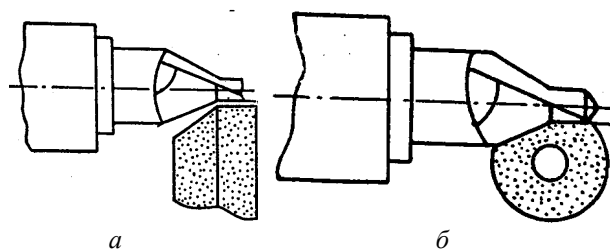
Схема обработки сверл шлифовальным кругом: а – шлифование по конусу и цилиндру; б – прорезка канавок
